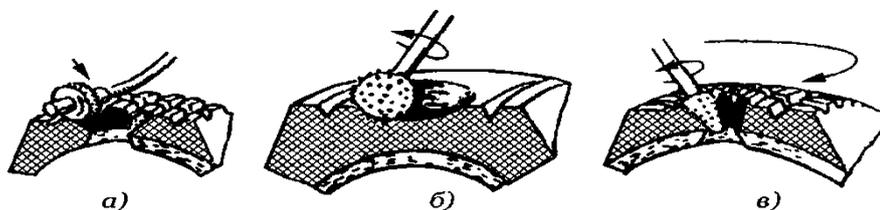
Обработка поврежденных участков шины шарошками различной конструкции: а — проволочной щеткой; б, в — фигурными шарошками
